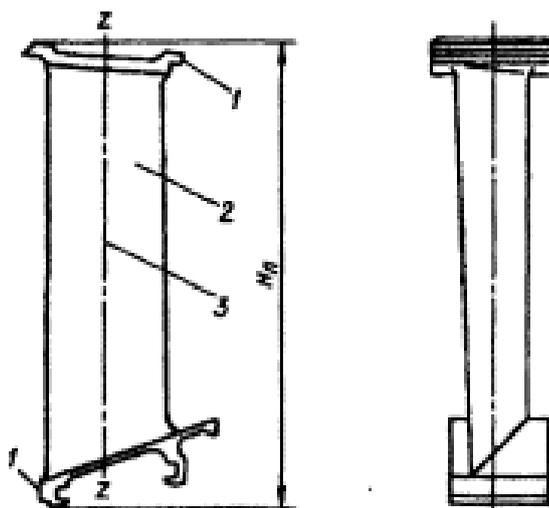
Направляющая лопатка статора компрессора: 1- хвостовик лопатки; 2 - перо лопатки; 3 - ось лопатки; $H_{л}$ — длина лопатки
